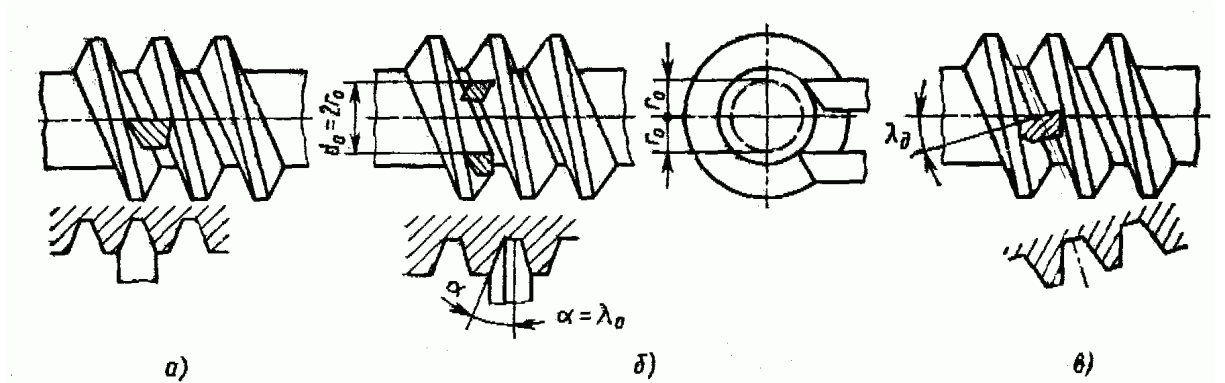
Схеми нарізання різцями черв'яків:
